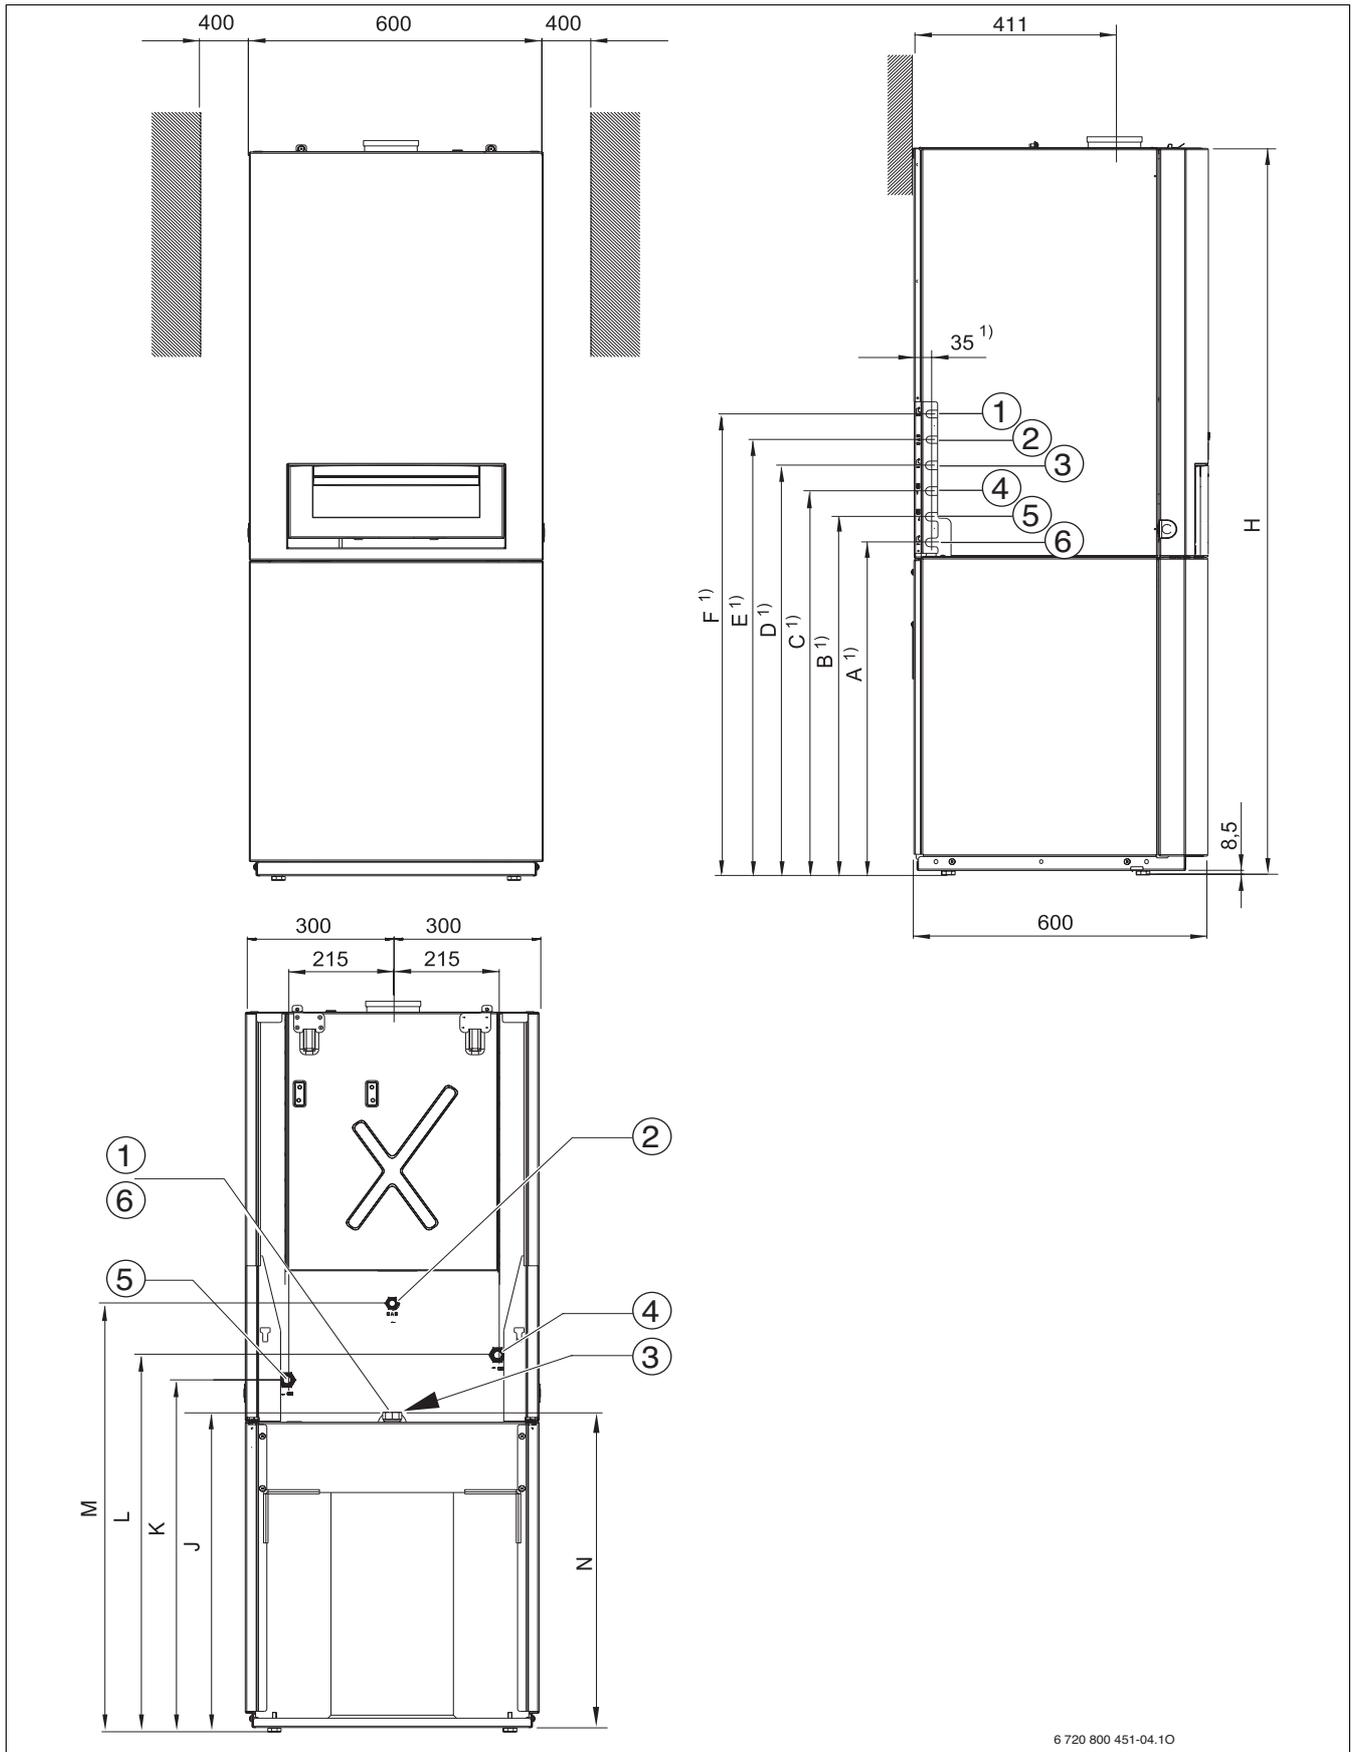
Dimensioni e attacchi per GB172-.. T150S (misure in mm)
